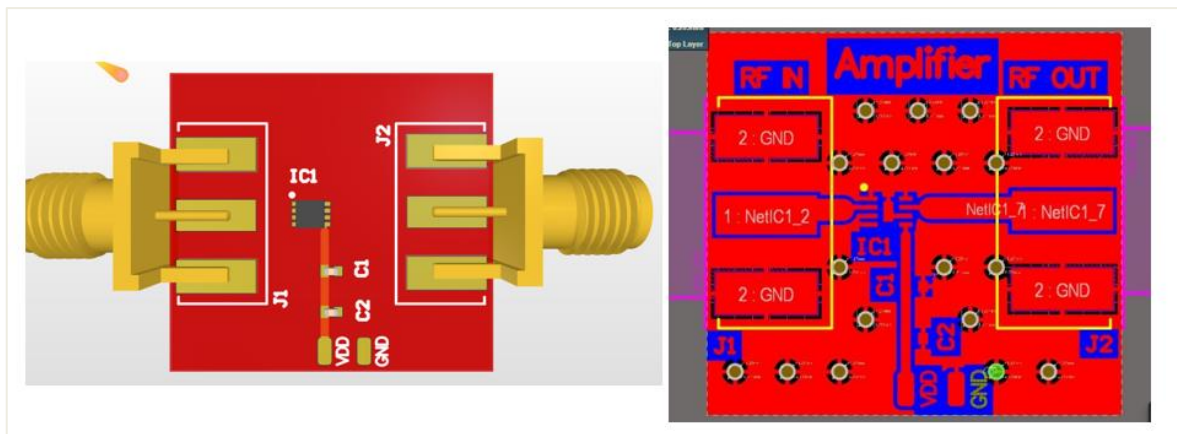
Diseño Final Amplificador Placa PCB.
